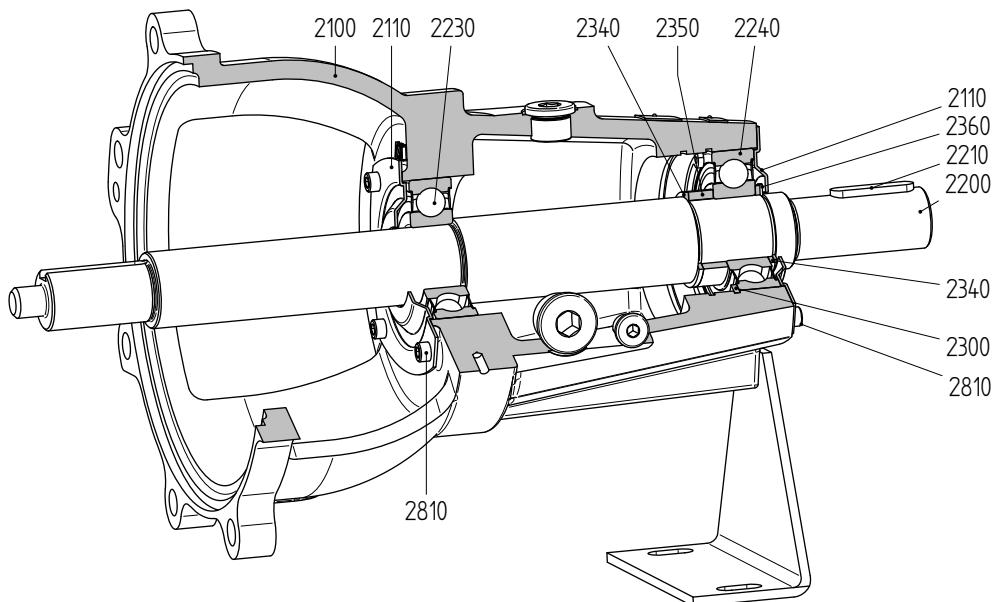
Подшипник L1 (стандартный, с консистентной смазкой)
